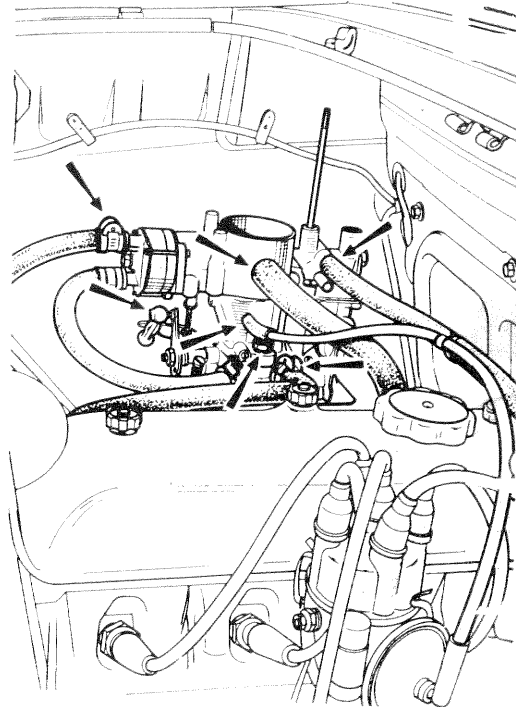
Points de débranchement pour le dépose du carburateur Solex
